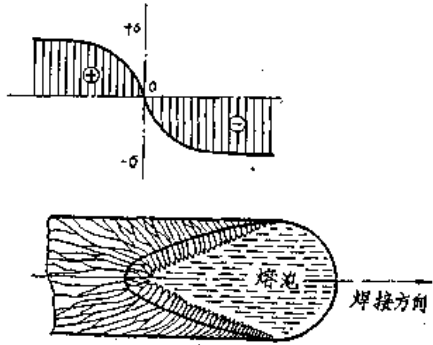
焊接时焊接接头金属的结晶与应力状态
